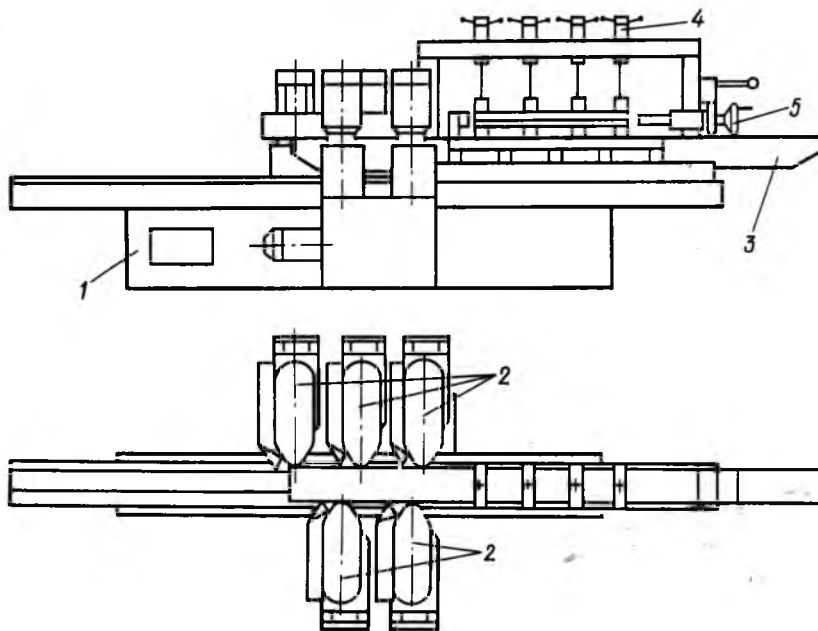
Общий вид фрезерно-копировального полуавтомата ФКД5: 1 — станина; 2 — фрезерные суппорты; 3 — каретка с копиями; 4 — прижимы; 5 — поворотное устройство
